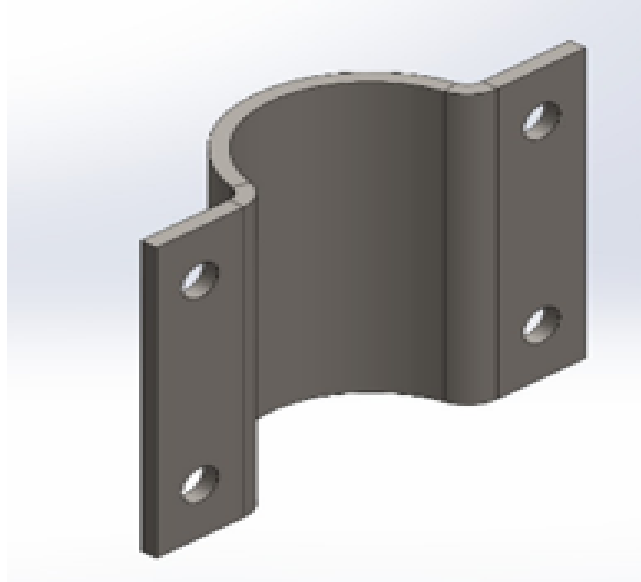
Soporte izquierdo del molde del pistón de 100cc
